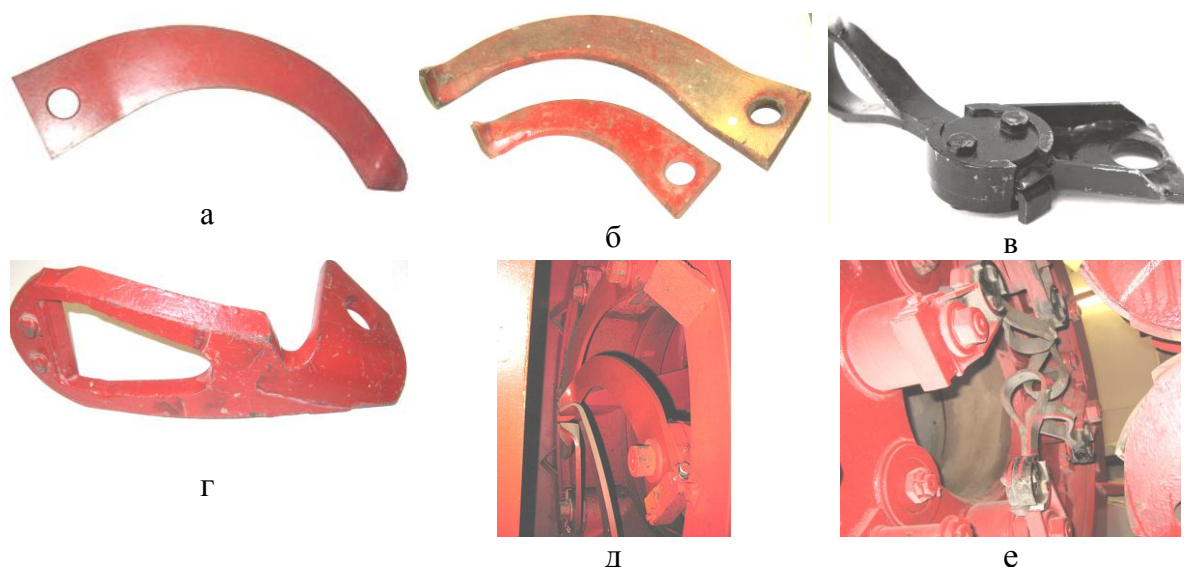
Коросниматели российских станков: а – ОК63; б – ОК63 и ОК40; в – петлевой коросниматель; г – зачистной нож; д – г-образные коросниматели в роторе ; е – петлевые коросниматели в роторе
